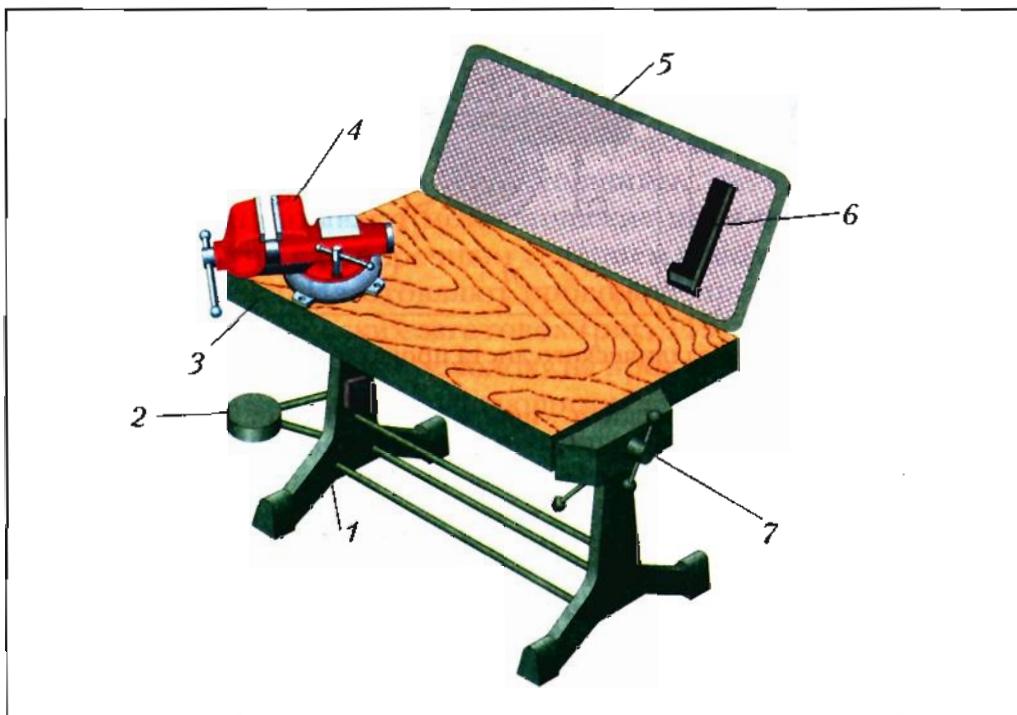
Универсальный верстак: 1 – основание; 2 – поворачивающееся сиденье; 3 – крышка; 4 – тиски; 5 – защитная сетка; 6 – подставка для документов; 7 – столярный зажим
